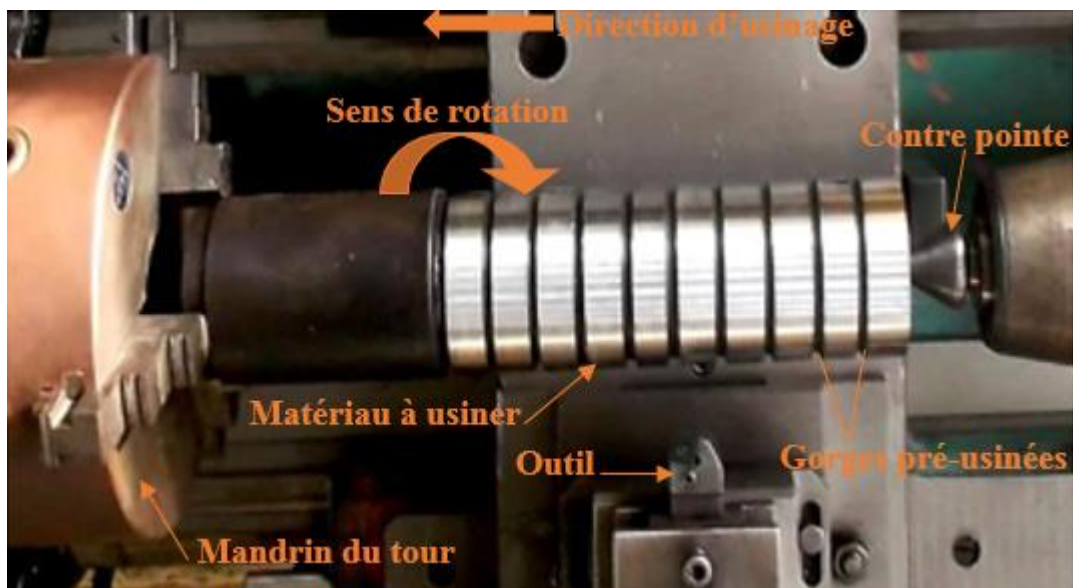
Représentation de l'éprouvette en montage d'usinage des essais de rugosité.
